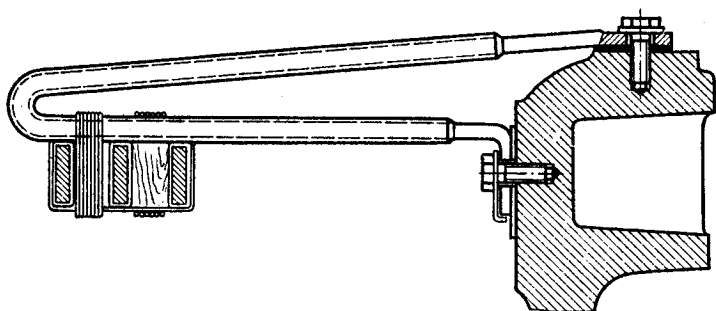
Крепление соединительных шин обмотки с поверхностным охлаждением к статору
